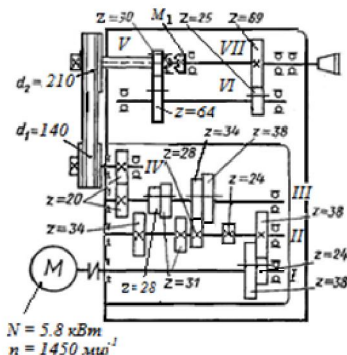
Кинематическая схема главного движения универсального консольно-фрезерного станка модели 6N81
